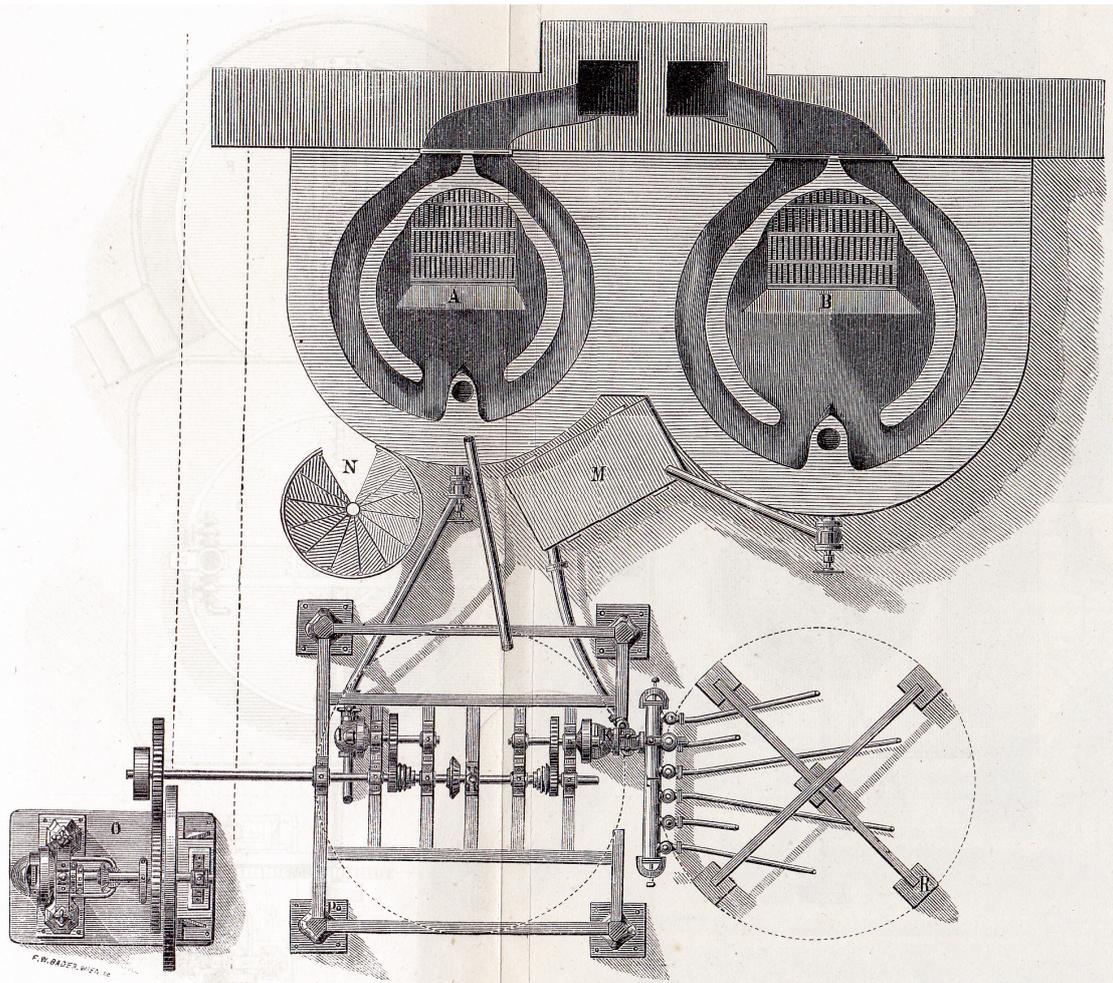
Grundriss des kompletten Brauapparats der Firma V. Prick im Jahr 1873 mit Warmwasserröhren
